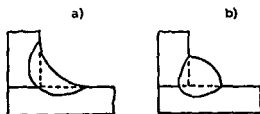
Soldaduras de filete (a) cóncava
